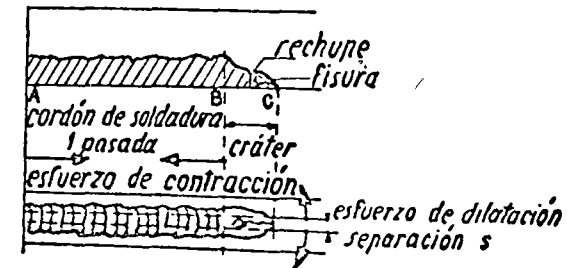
Interpretación del agrietamiento en el cráter terminal de una soldadura por arco.
